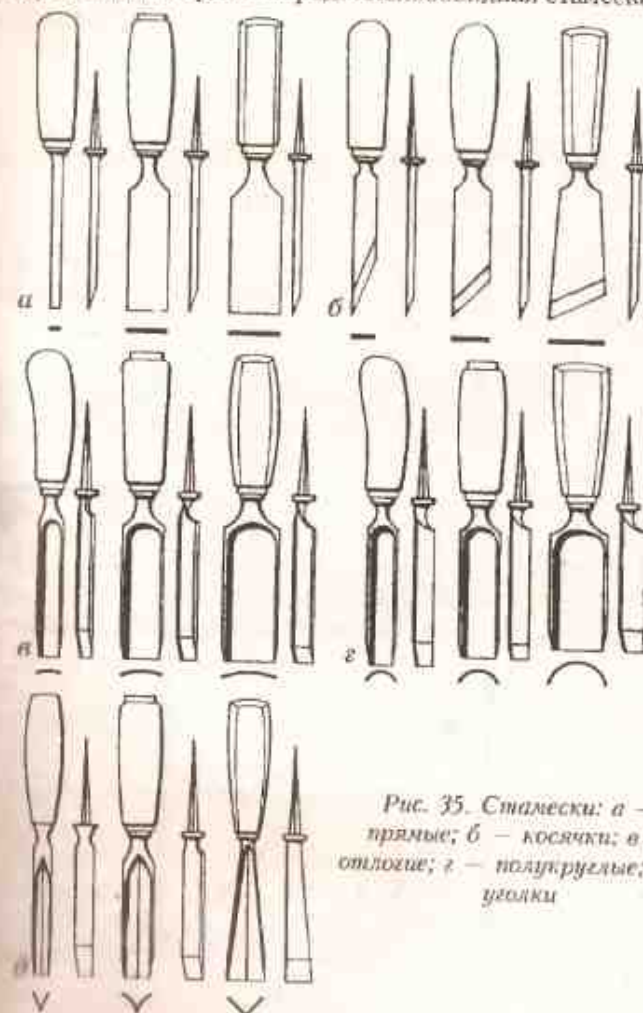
Стамески: а — прямые; б — косычки; в — отлогие; г — полукруглые; д — уголки
